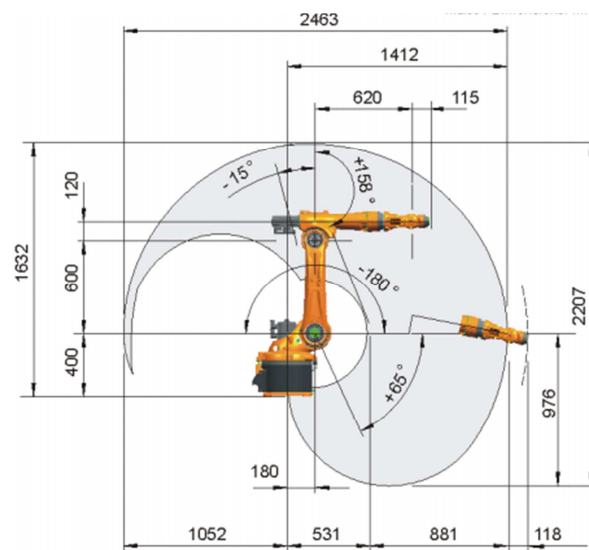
Dimensiones del Robot KR 5ARC (KUKA Roboter GmbH, 2009)
